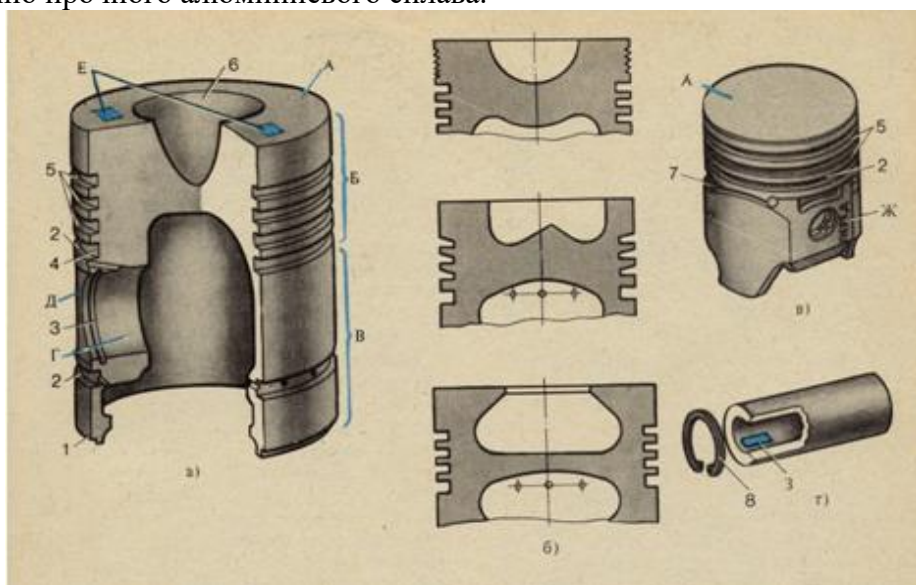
Конструкция поршня: а - поршень дизельного двигателя, б - сечения поршней дизельных двигателей, в - поршень карбюраторного двигателя, г - поршневой палец, 1 - маслосбрасывающая кромка, 2 - канавка для маслосъемного кольца, 3 - канавка для стопорного кольца, 4 - отверстие для подвода масла к поршневому пальцу, 5 - канавки для компрессионных колец, 6 - камера сгорания в поршне, 7 - прорезь, 8 - стопорное кольцо поршневого пальца; А - днище, Б - головка, В - направляющая часть, Г - бобышки, Д - холодильник, Е - места клеймения массы и размерной группы поршня, Ж - метка направления установки поршня, З - место клеймения размерной группы поршневого пальца.
